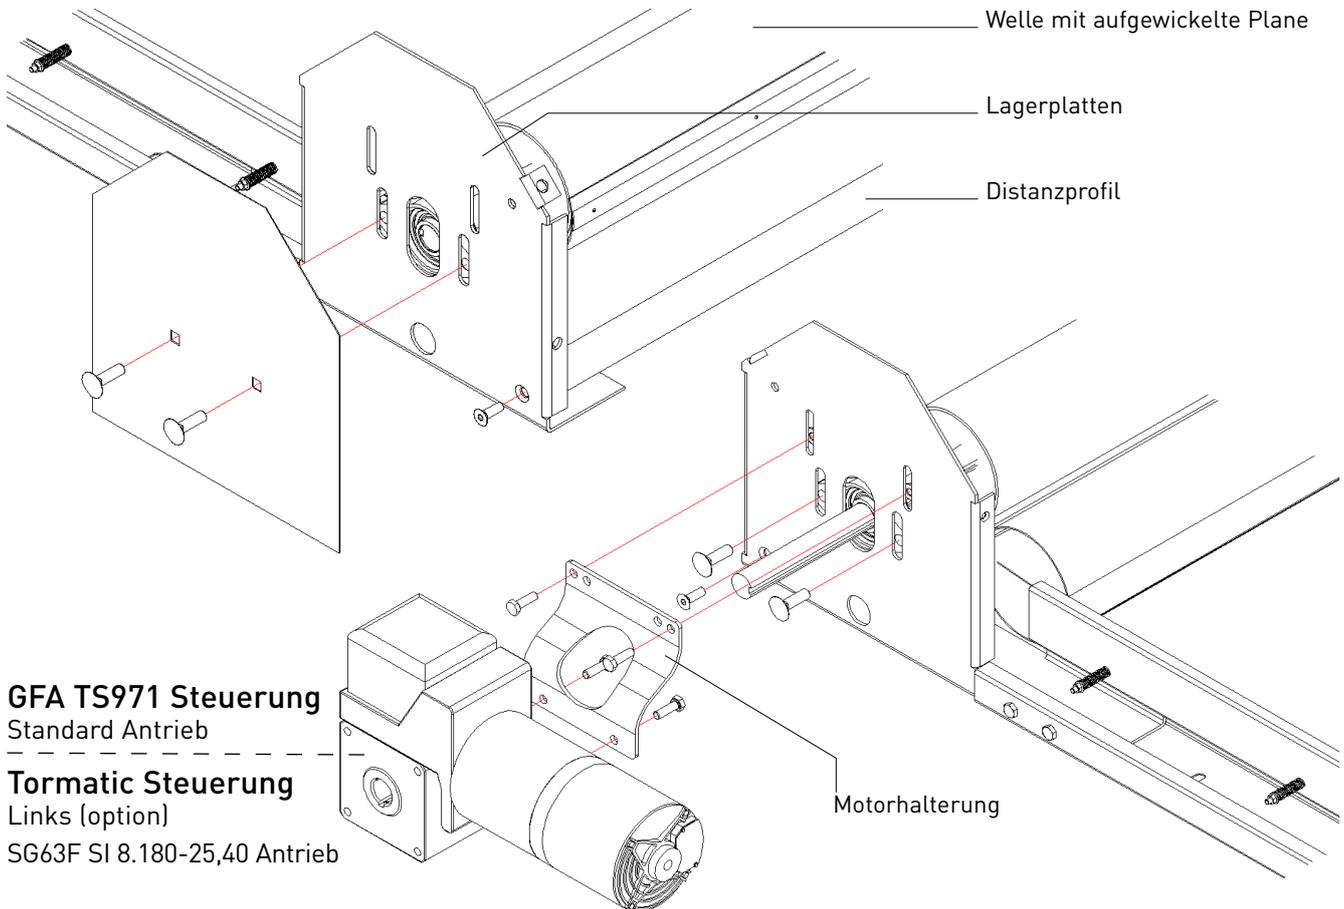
Zusammenschrauben der Wellenbaugruppen
